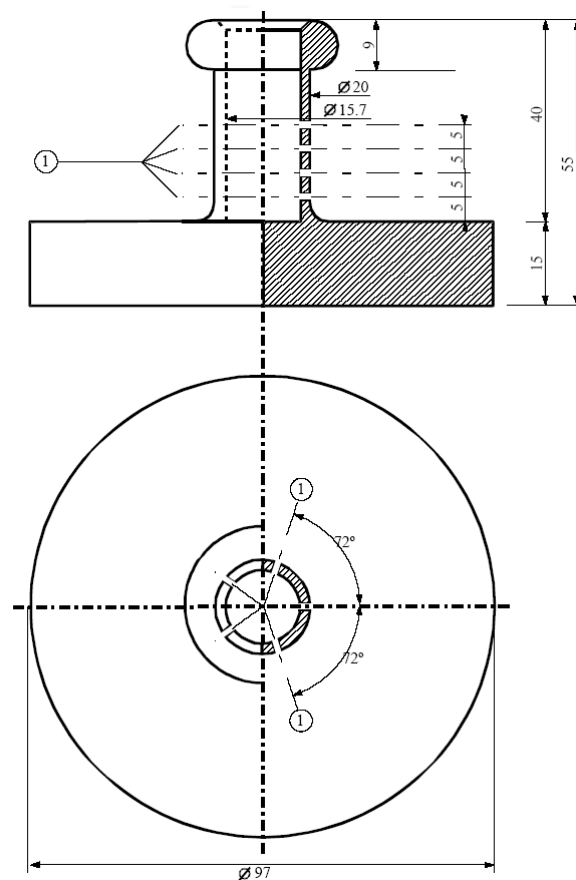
Cilindro cavo di bronzo, chiuso da un lato; vista in pianta e sezione verticale
